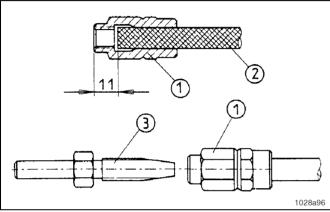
Предварительный монтаж резьбовых гильз и патрубков шланга на высоконапорном шланге
